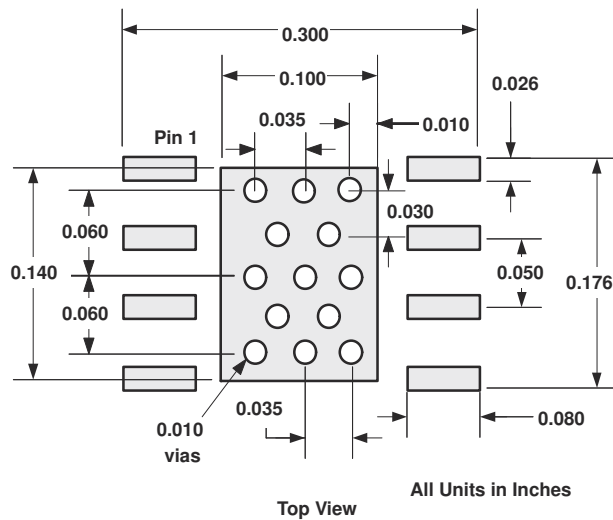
DDA PowerPAD™ 集成电路封装 PCB 蚀刻和过孔布局
